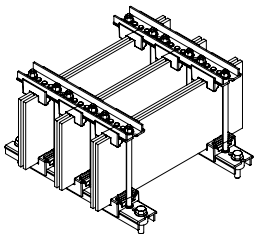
Инструкция по сборке шинодержателя / Figure 3 – The instructions for assembling the bus holder / 3 сурет – Шина ұстатқышты құрастыру жөніндегі нұсқаулық
